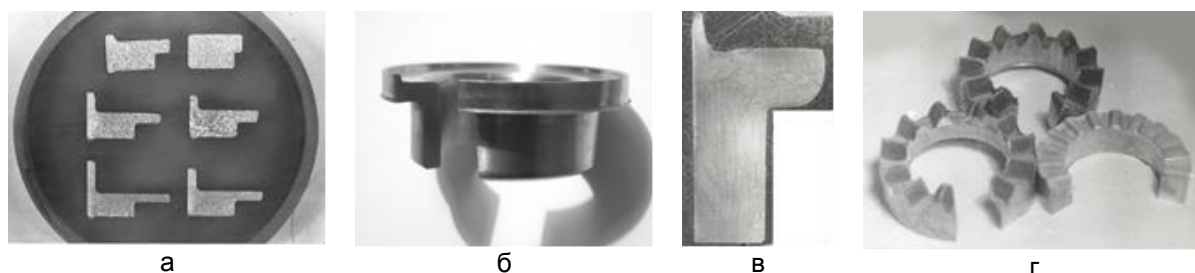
Загальний вигляд і перерізи заготовок, сформованих методами ШО за схемами прямого і зворотного витискування: а) перерізи заготовок із міді М06, деформованих до різних ступенів за схемою 1,а; б) заготовка із сталі 14Х17Н2, сформована за схемою 1,б; в) переріз заготовки із сталі 30ХГСА, деформованої за схемою аналогічною 1,б, але з формуванням внутрішнього бурта; г) заготовки із міді М06, деформовані до різних ступенів за схемою 1,в
